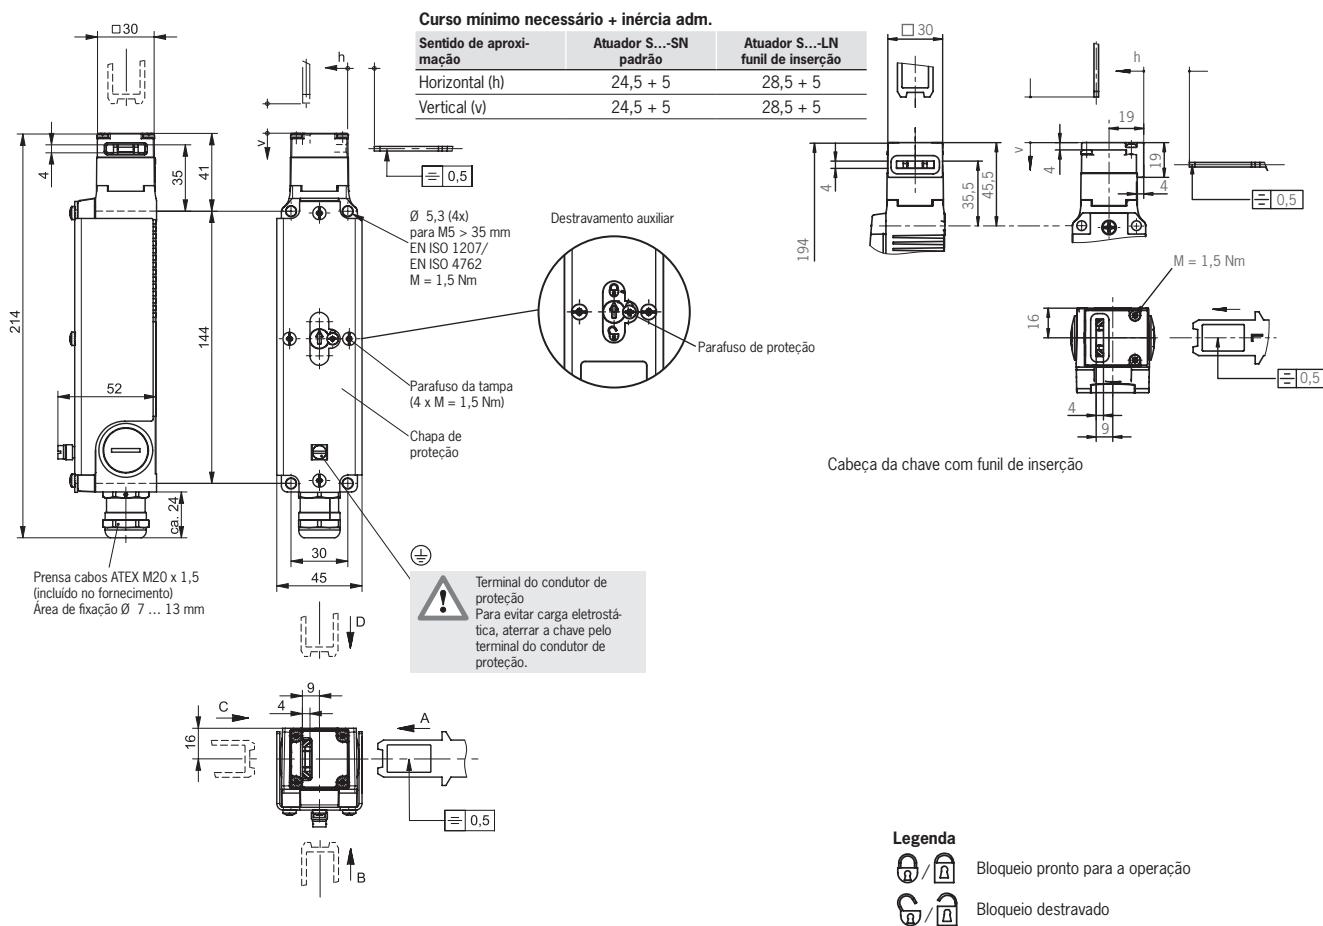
Desenho dimensional STA... sem funil de inserção e STA... com funil de inserção
